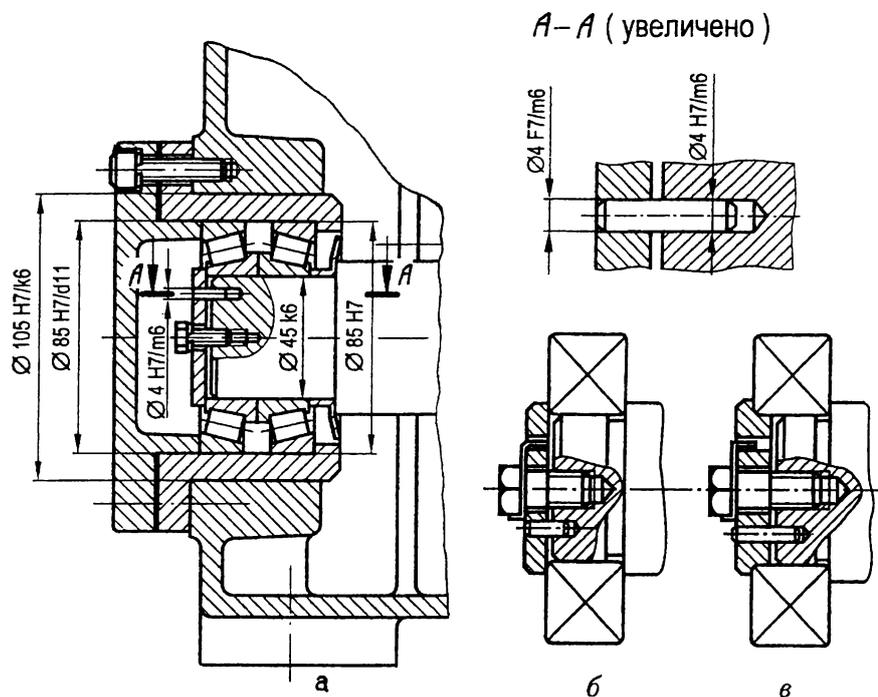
Пример конструкции подшипникового узла с деталями для регулирования осевого зазора в подшипниках и крепления их внутренних и наружных колец
